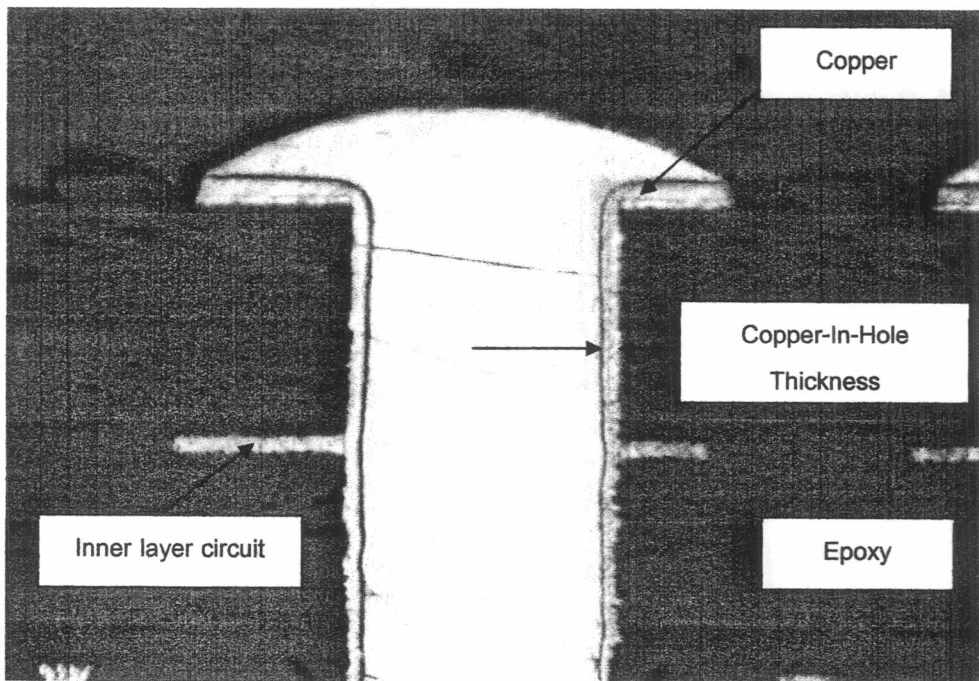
แสดงตัวอย่างแผ่น PCB
